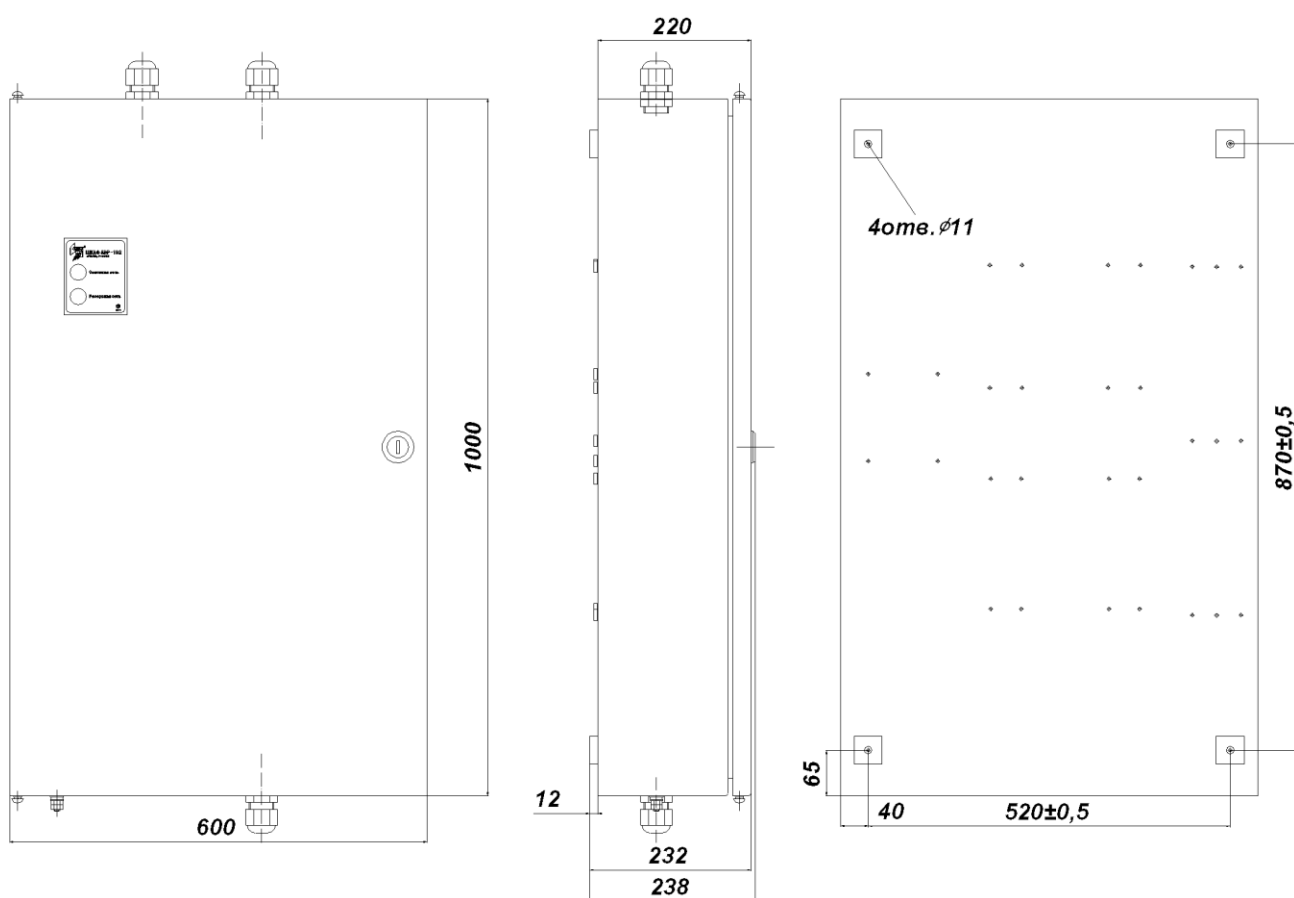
Габаритный чертеж Шкафа с установочными размерами
